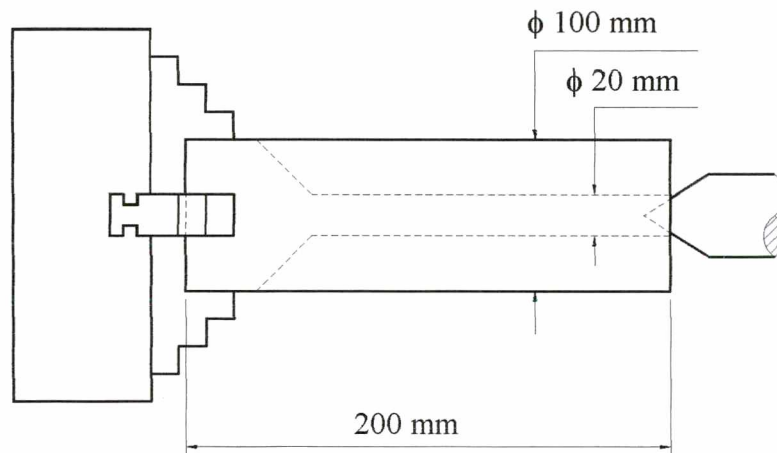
Representação esquemática da fixação do corpo de prova na máquina-ferramenta e dimensões inicial e final do mesmo
